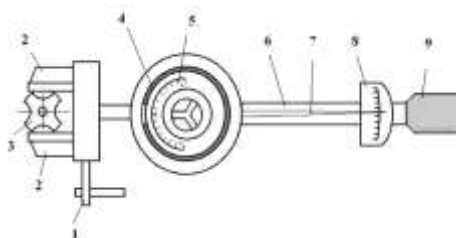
Устройство люфтомера-динамометра: 1 – винтовой зажим; 2 – подвижные губки; 3 – фланец крестовины; 4 – жидкостный уровень; 5 – градуированная шкала; 6 – рессорный элемент динамометра; 7 – стрелка динамометра; 8 – шкала динамометра; 9 – рукоятка
